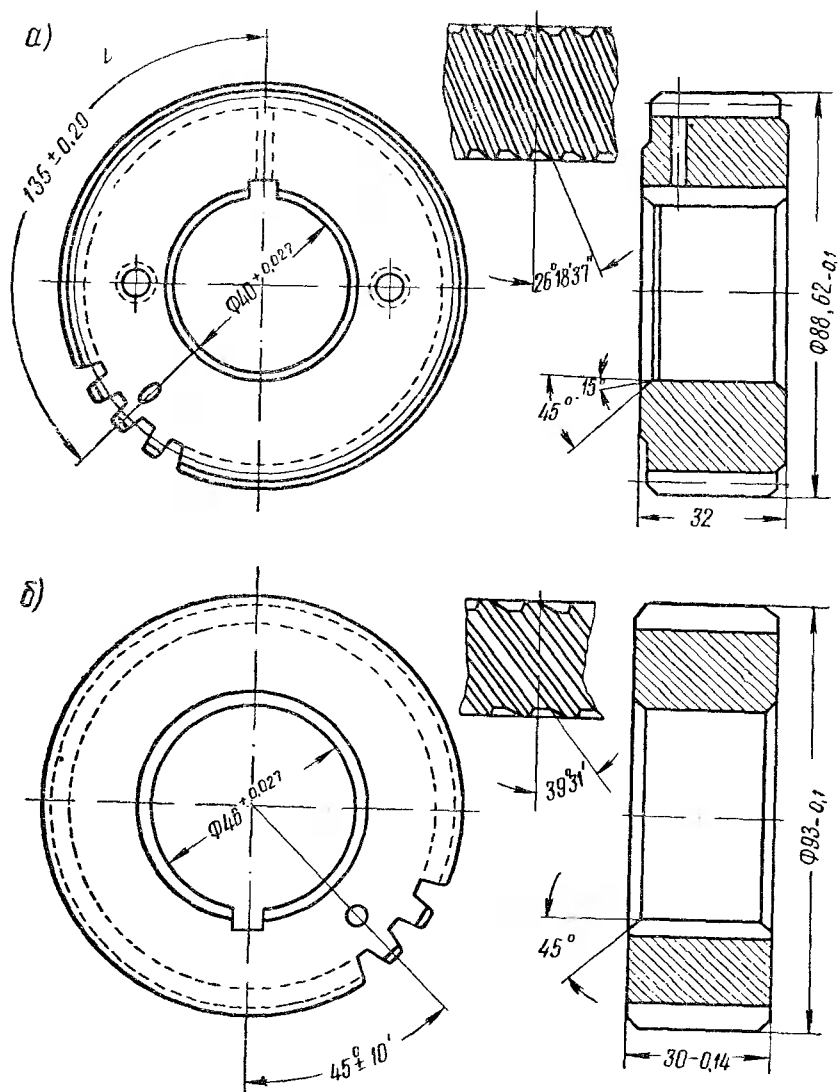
Шестерни газораспределения коленчатых валов двигателей:
